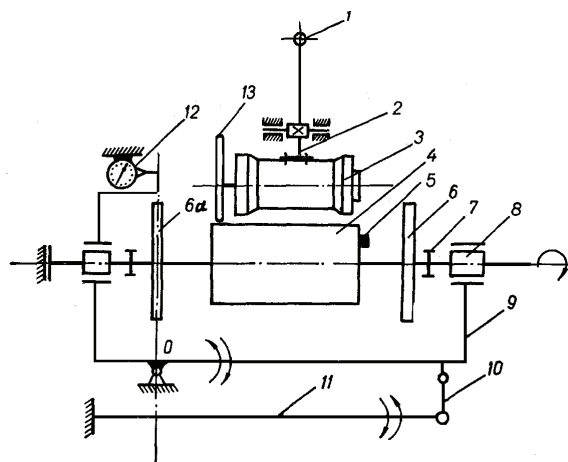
Кинематическая схема балансировочного стенда: 1 — рукоятка; 2 — рычаг; 3 — вал электродвигателя; 4 — ротор; 5 — болт; 6, 6а — динамически отбалансированные диски; 7 — винты; 8 — подшипники; 9 — маятниковая рама; 10 — серьга; 11 — пружина; 12 — индикатор часового типа; 13 — фрикционное колесо
